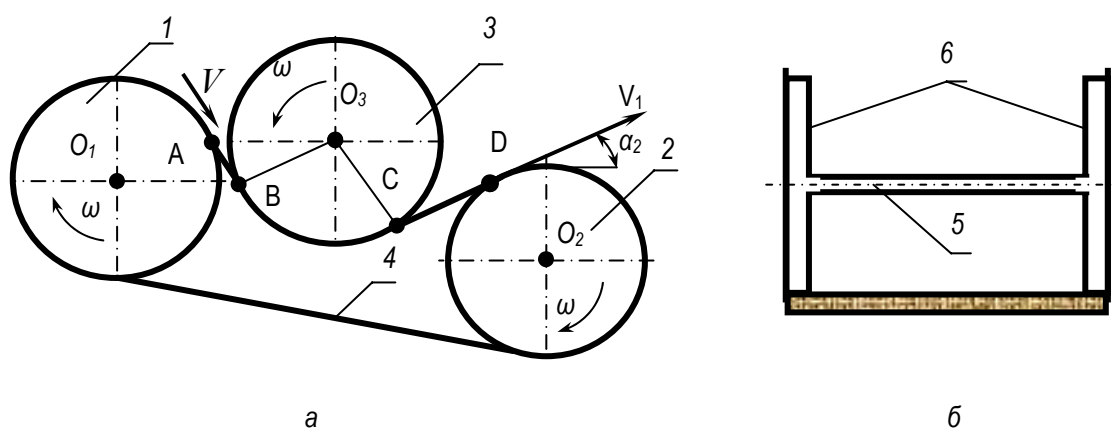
Схема ленточного зернометателя с полым прижимным барабаном:
